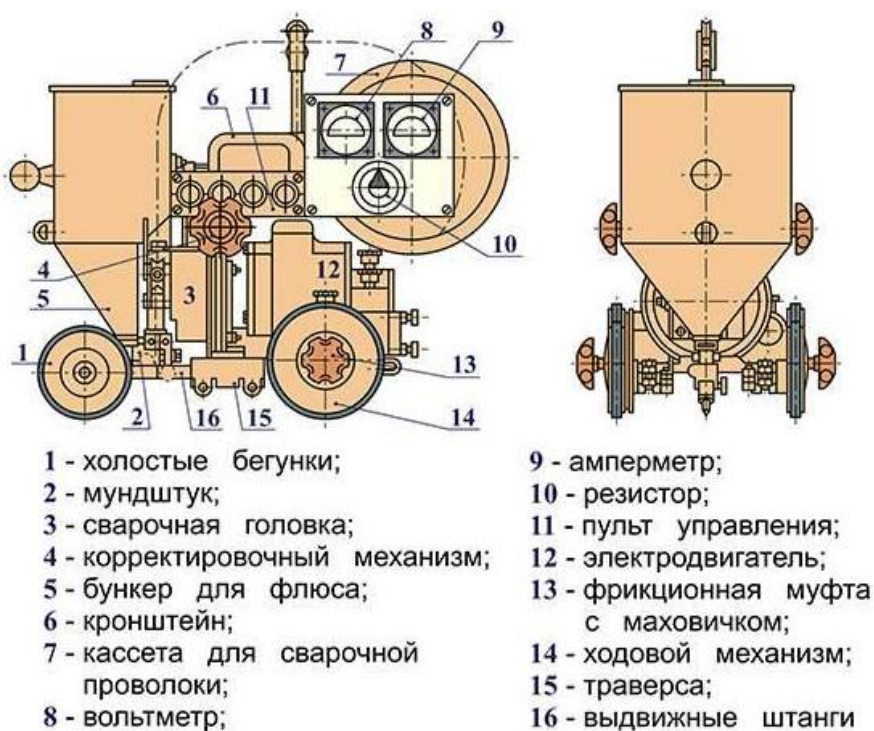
Конструкция сварочного трактора для сварки под флюсом
